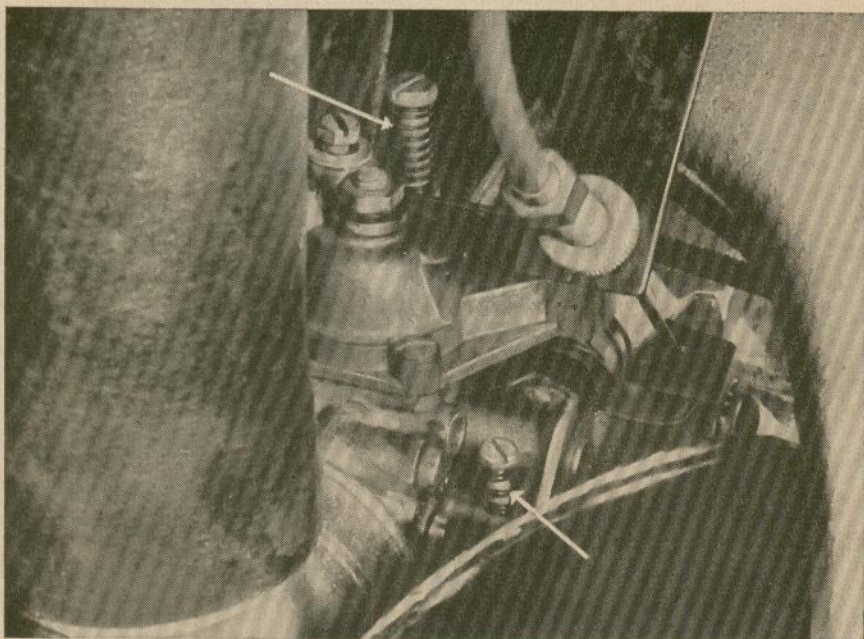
Drosselklappenanschlagschraube (unten) und Regulierschraube für die Leerlaufmischmenge (oben)
